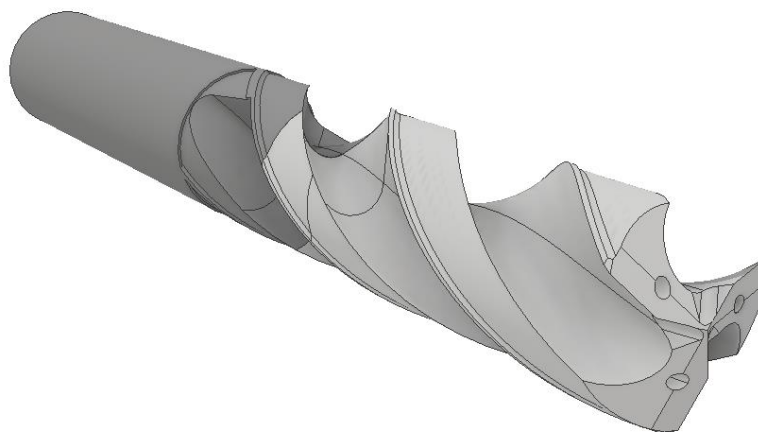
Свердло 3HD 100-035-10 P13
